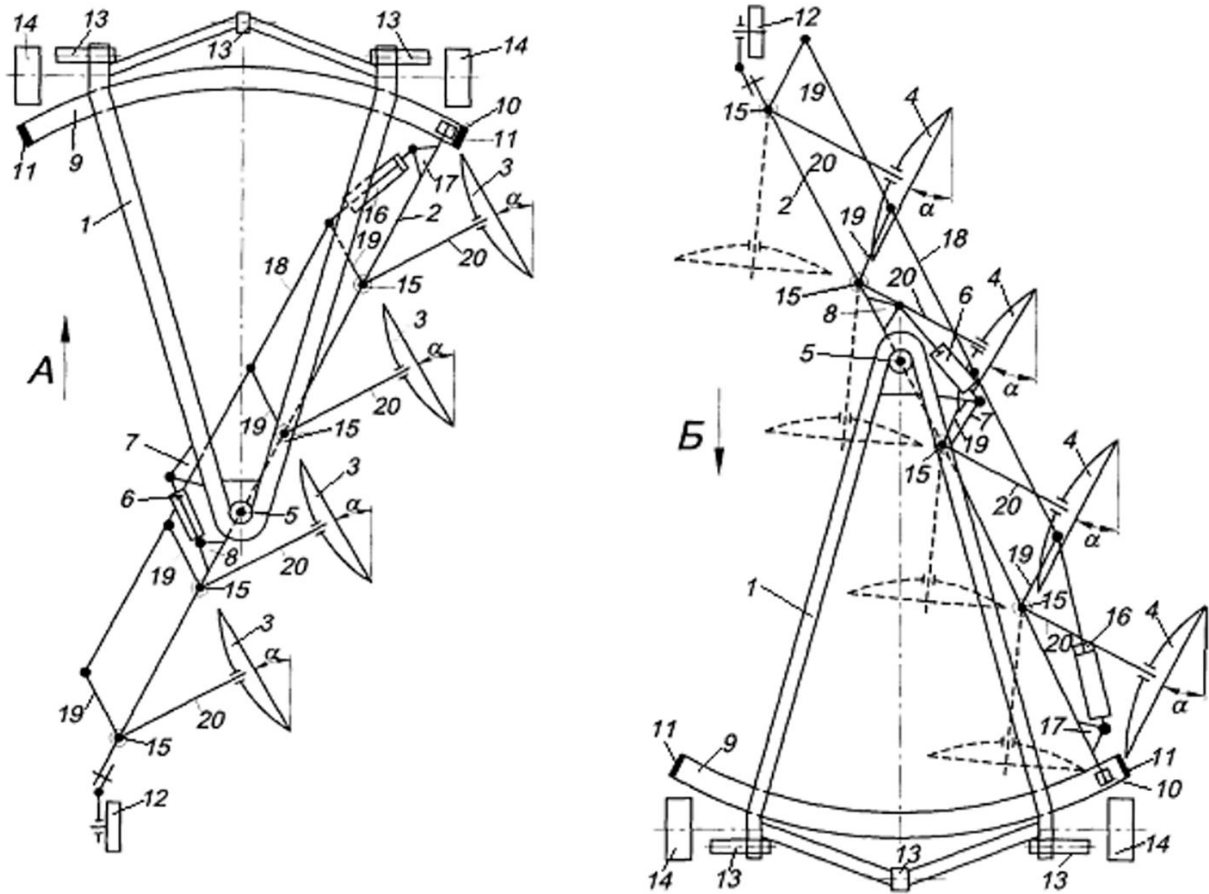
Поворотний дисковий плуг для гладкої оранки [88]
